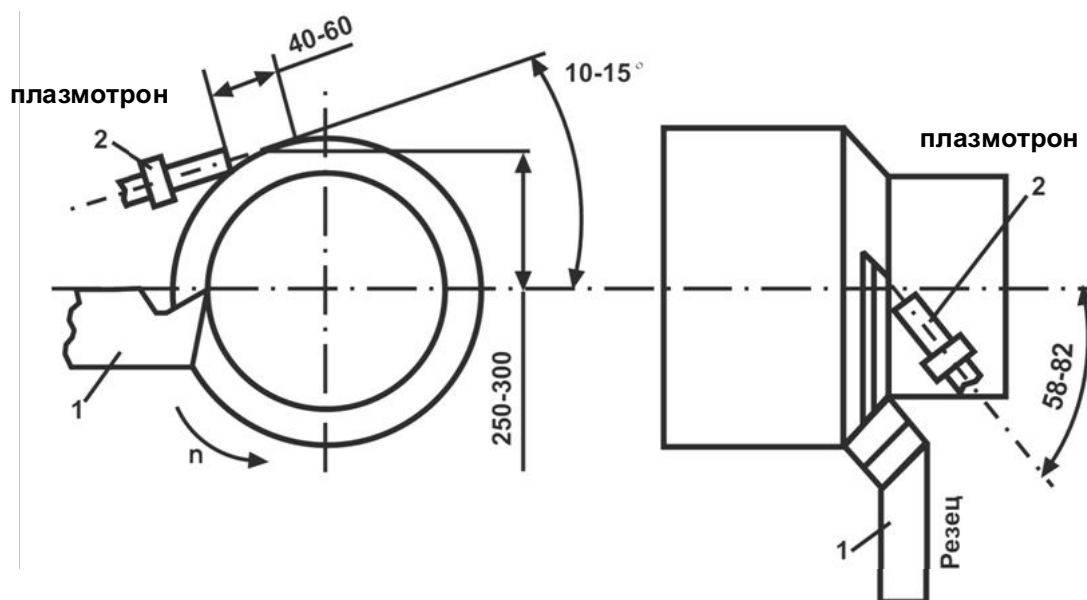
Схема установки плазмотрона относительно обрабатываемой заготовки
